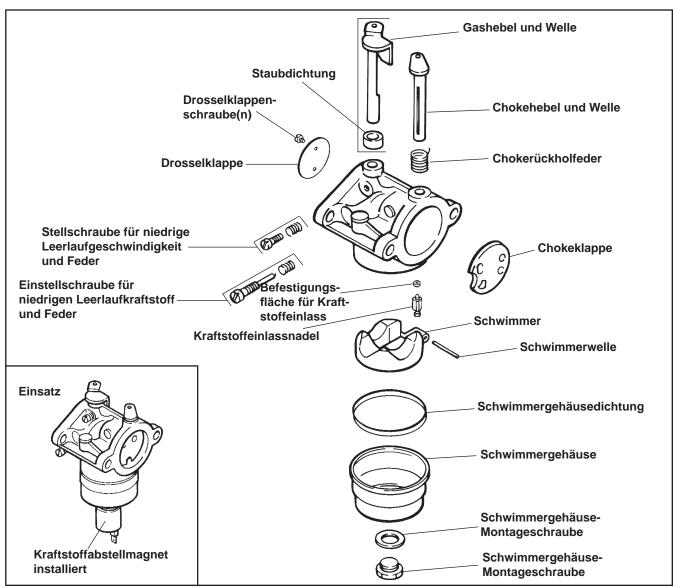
Vergaser mit verstellbarer Hauptdüse - Explosionszeichnung.
